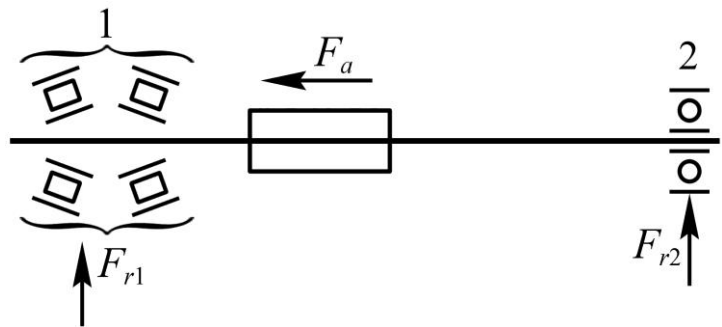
Вал зі здвоєними радіально-упорними підшипниками
